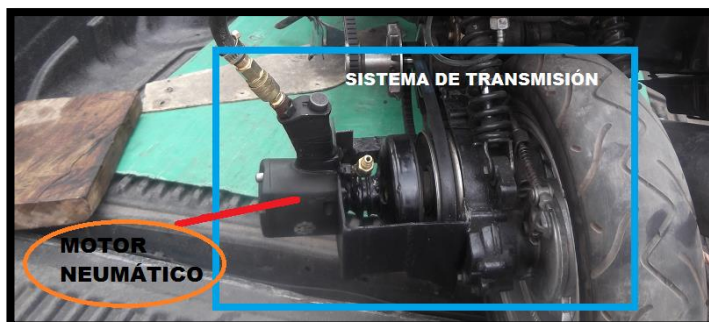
Pistola de impacto instalada en la motocicleta.
